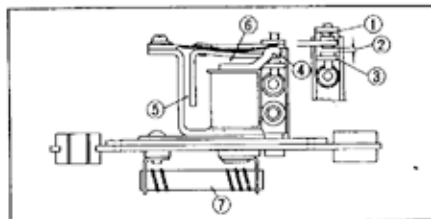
① Cavetti gialli. ② Cavetto rosso/bianco. ③ Cavetto verde.
